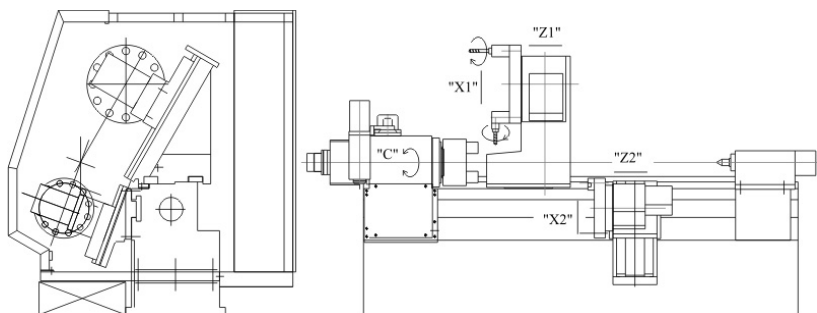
Центр токарный двухсуппортный, с устройством позиционирования и круговой подачи шпинделя (осью С), револьверными головками для токарного и приводного инструмента на верхнем и нижнем суппортах
